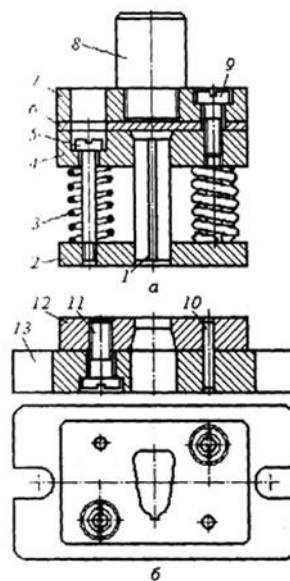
Простий штамп для пробивання пазів в листі статора
